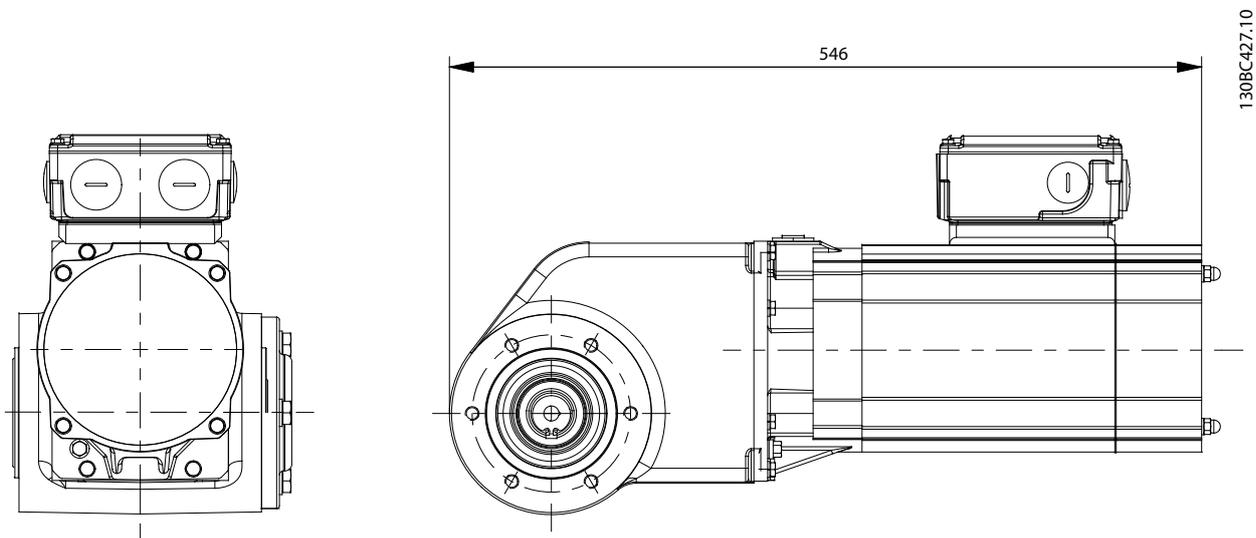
Dimensions du VLT® OneGearDrive avec option de frein mécanique
